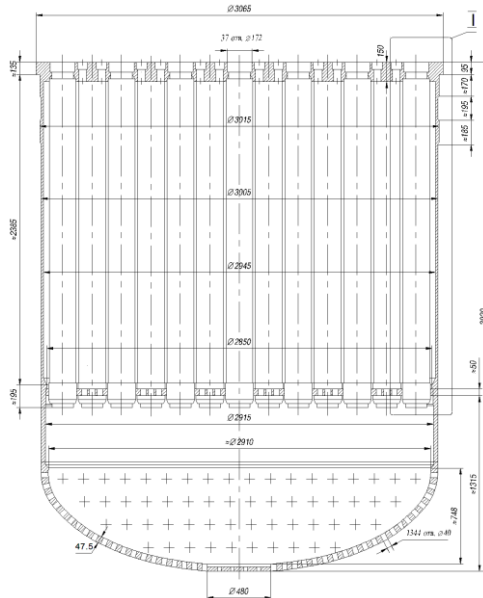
Общий вид днища шахты ВВЭР-440
